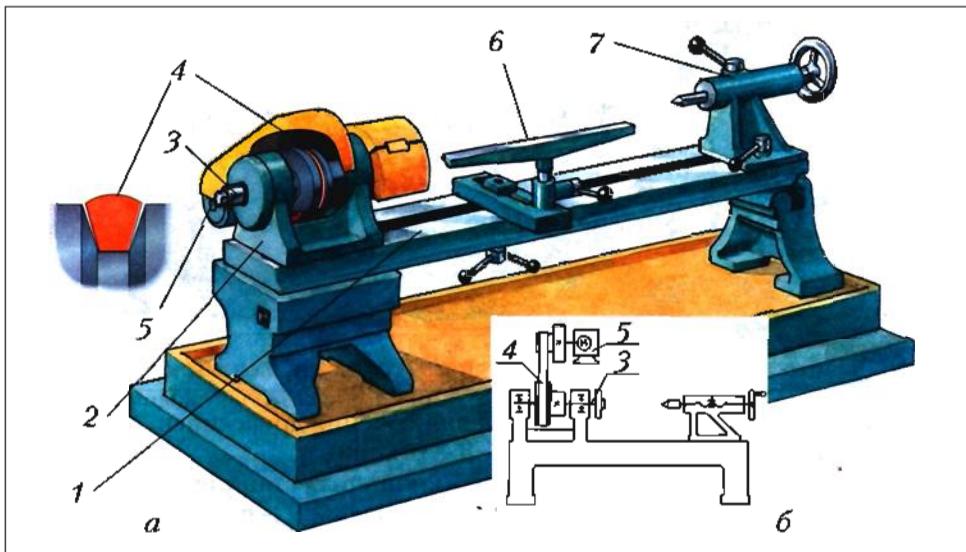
Токарный станок ТД-120 для точения древесины: *а* – общий вид, *б* – кинематическая схема; 1 – направляющие, 2 – передняя бабка, 3 – шпиндель, 4 – клиноременная передача, 5 – электродвигатель, 6 – каретка с подручником, 7 – задняя бабка
